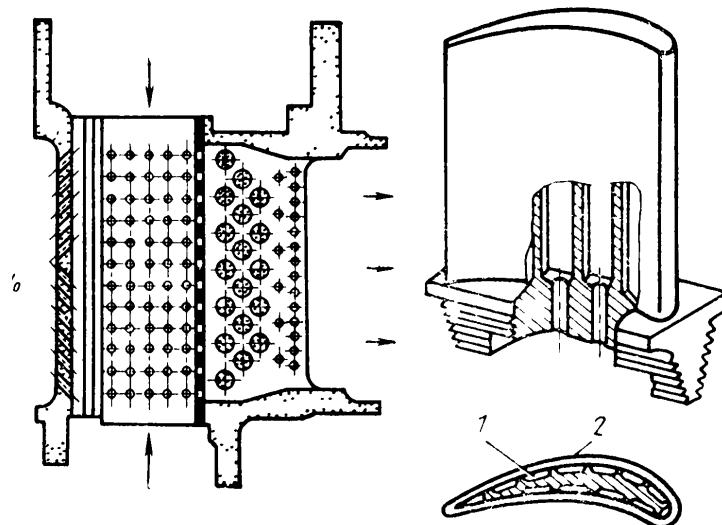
Схема лопатки с пористым охлаждением: 1 - несущий стержень; 2 - оболочка из пористого материала
